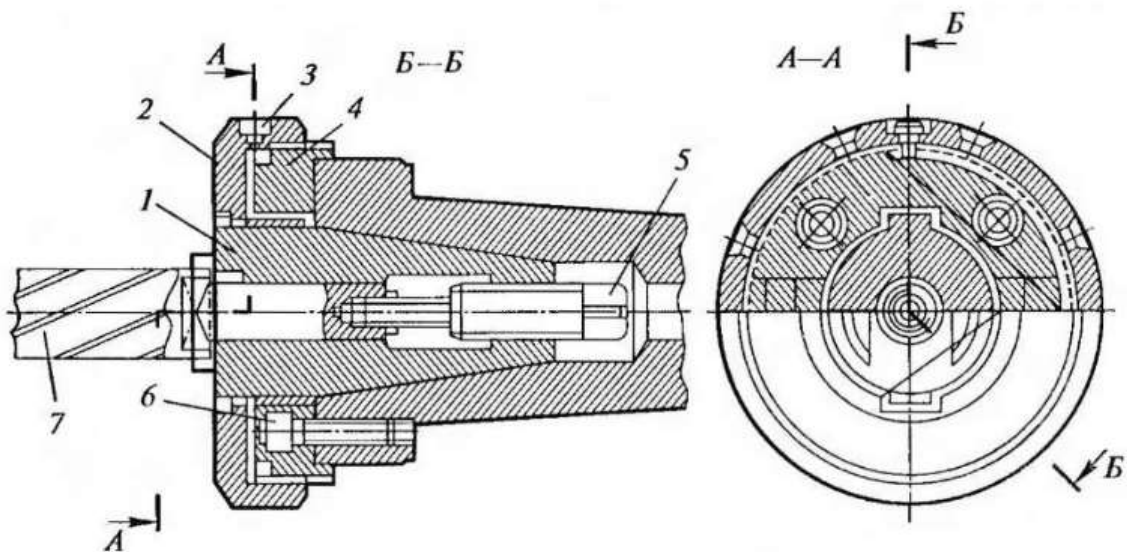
Швидкодіючий патрон для фрез: 1 – втулка; 2 – гайка; 3, 5, 6 – гвинти; 4 – перехідний фланець; 7 – фреза
